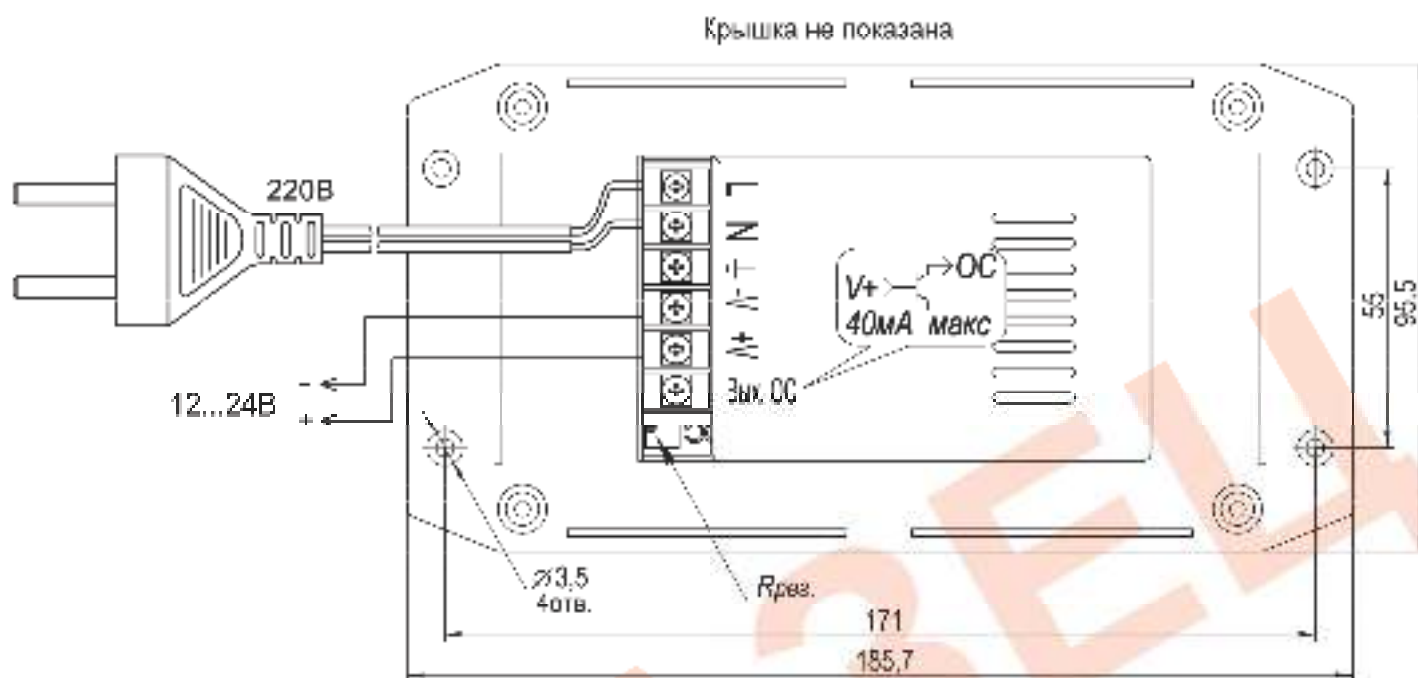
Устройство, габаритные и установочные размеры, подключение изделия
